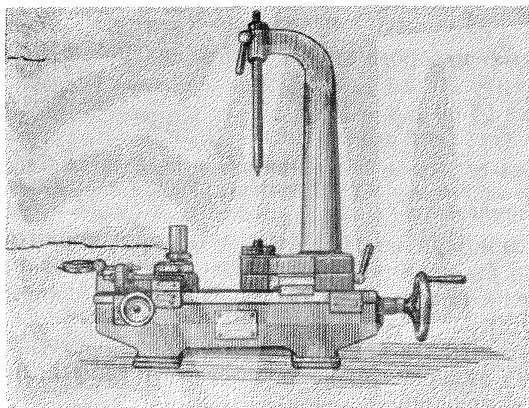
Межцентромер с кронштейном для проверки валковых колес
